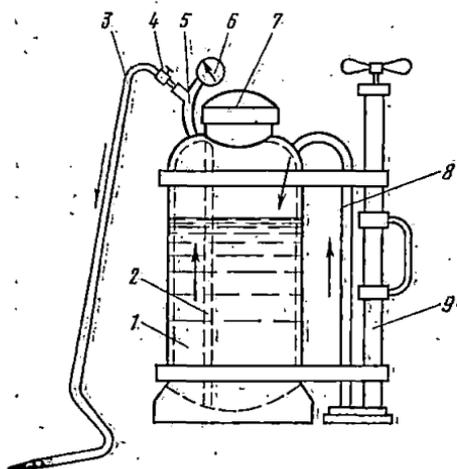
Приспособление для промывки конденсаторов воздушного охлаждения:
